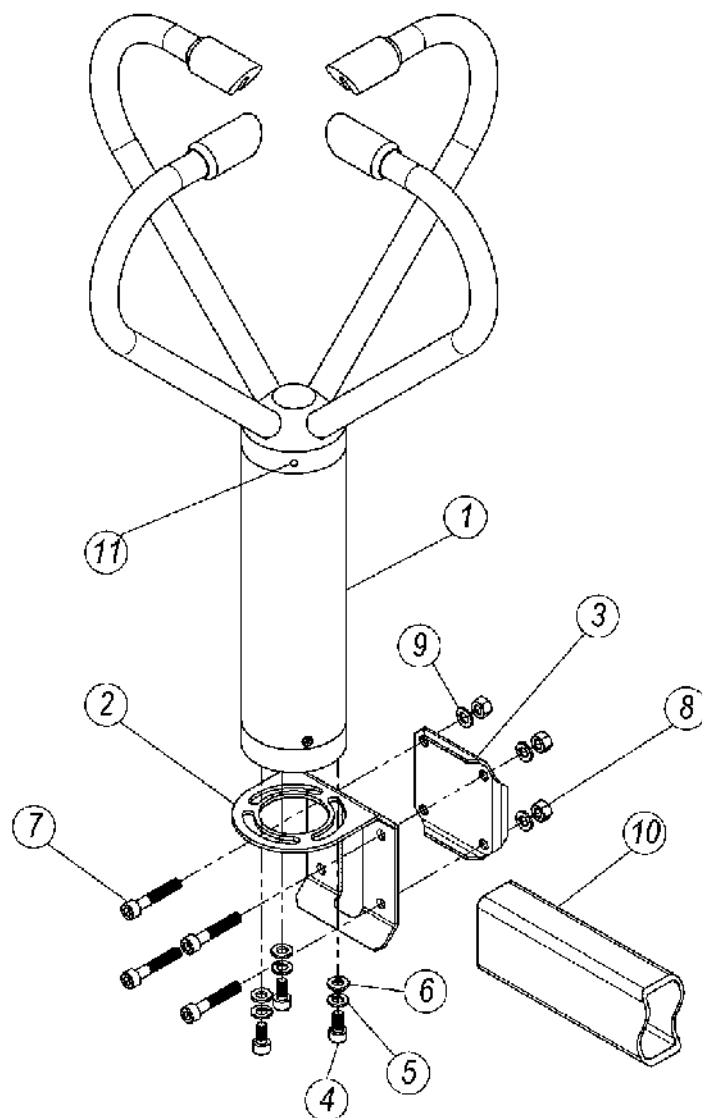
Крепление датчика на монтажном кронштейне или траверсе: 1 – датчик; 2 – кронштейн крепления; 3 – скоба крепления; 4 – винты крепления; 5, 9 – пружинные шайбы; 6 – шайбы; 7, 8 – болты и гайки крепления; 10 – монтажный кронштейн или траверса; 11 – метка направления на север.
